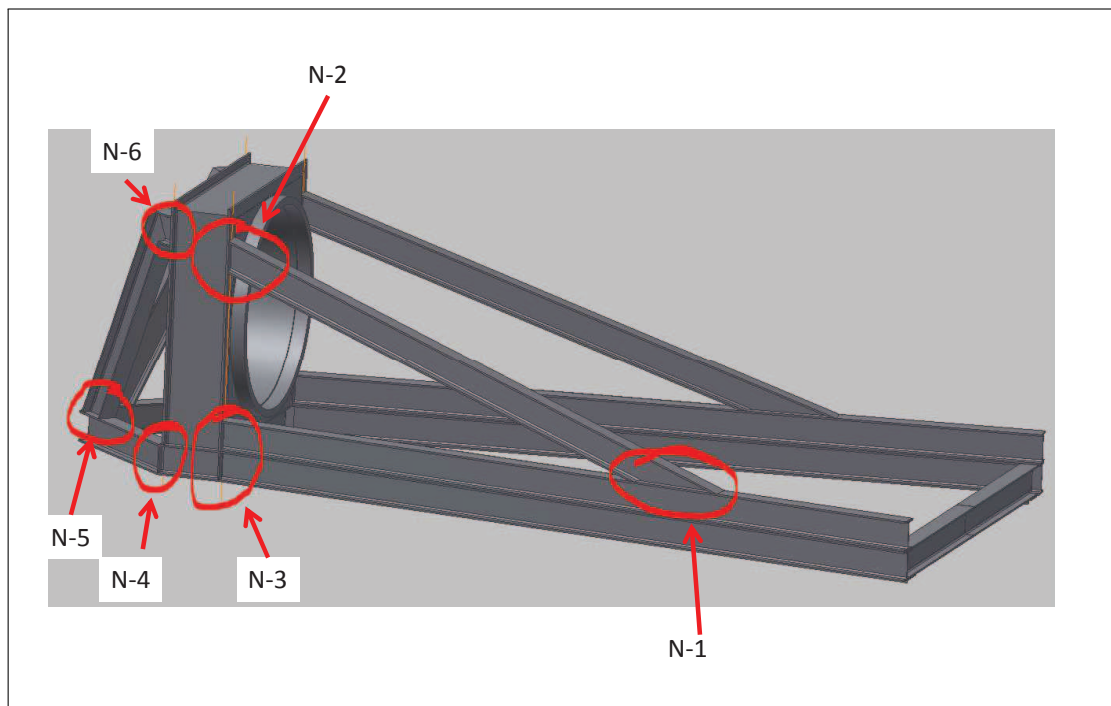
Übersicht über die nachgerechneten Schweißnähte N-1 bis N-6
